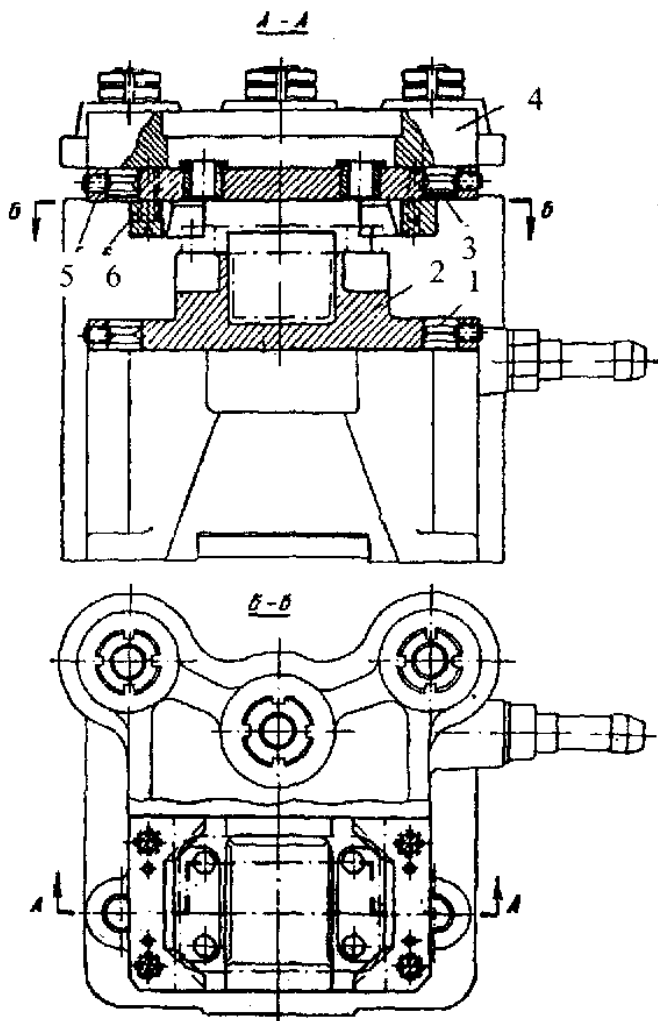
Приклад базування і закріплення змінного налагодження на корпусі кондуктора
